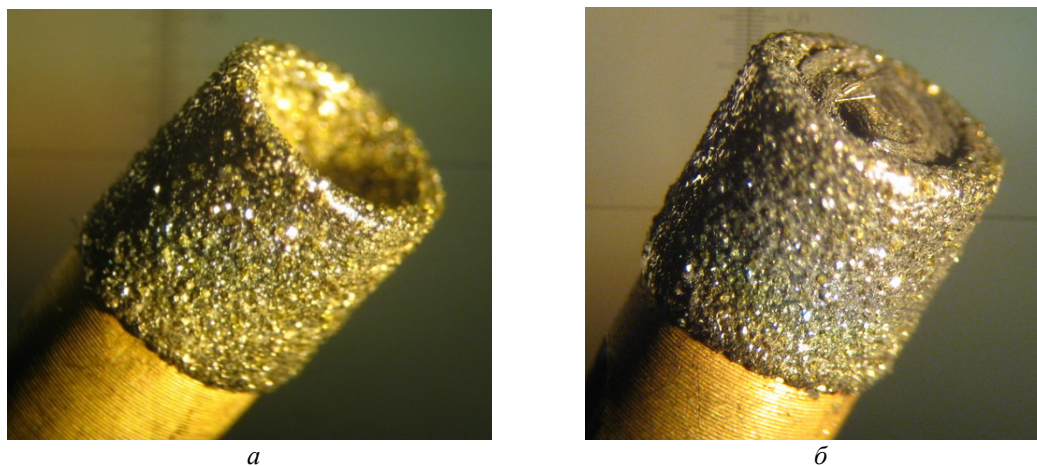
Засаливание и забивание кольцевого сверла при сверлении углепластика: не использованное (а); после сверления нескольких отверстий (б)
